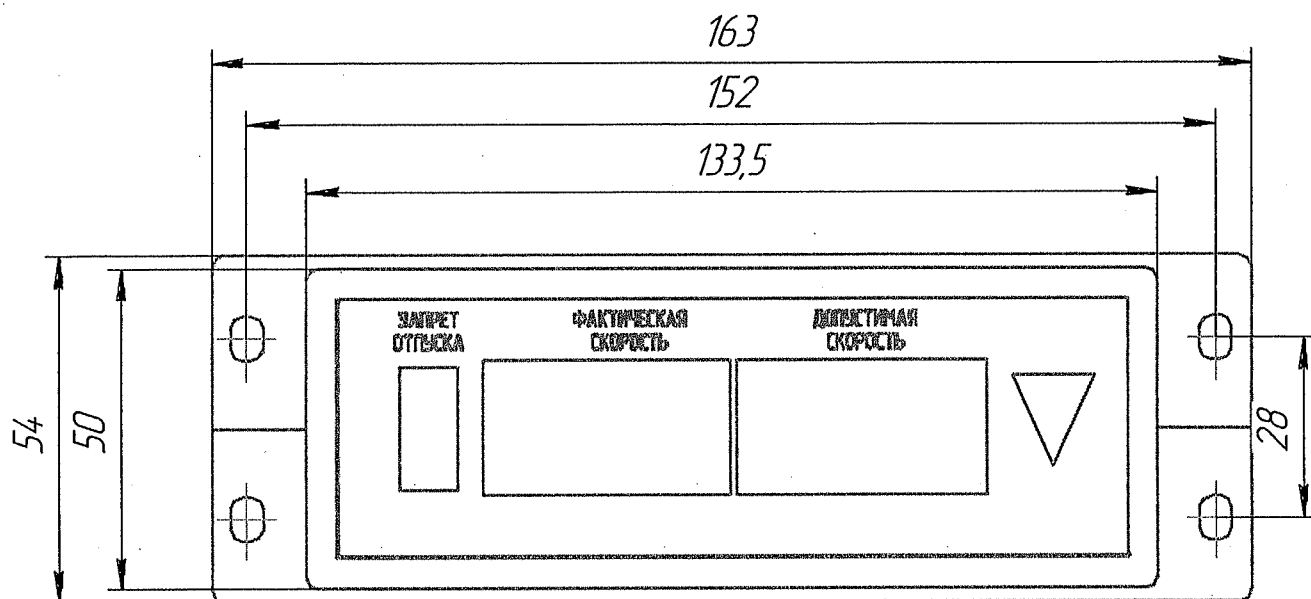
Внешний вид и присоединительные размеры блока БИЛ-ИП-03,
